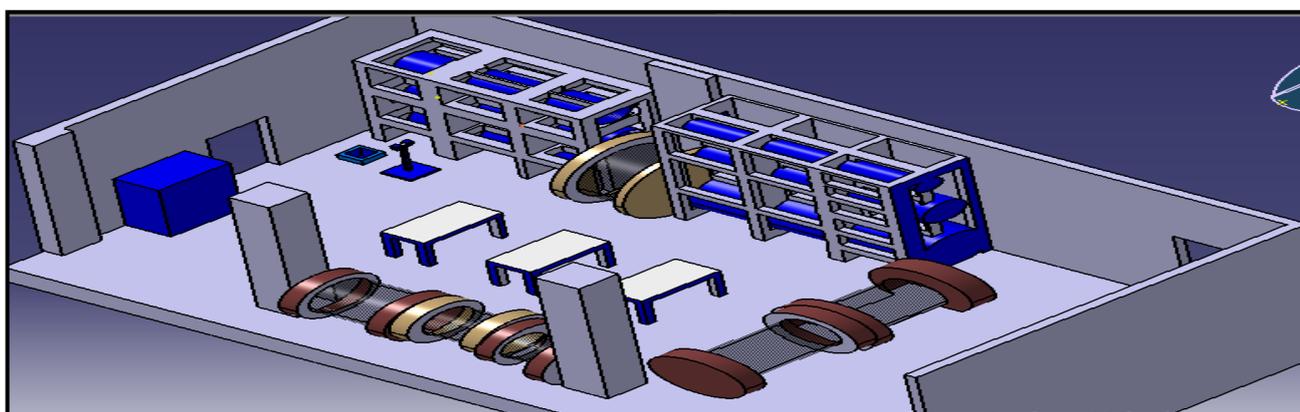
La nouvelle zone de coupe et d'assemblage des câbles de grosse section
